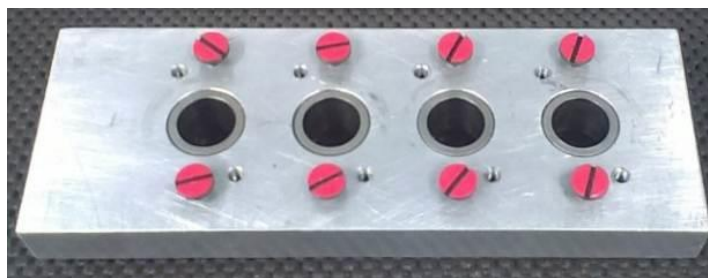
Накладной кондуктор для Atlas Corco PFD-1500
